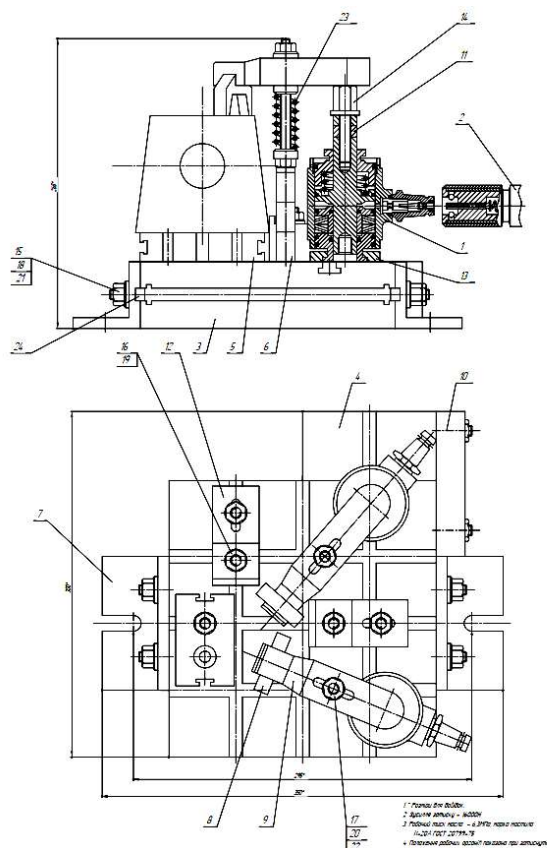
Схема верстатного пристрою для фрезерування
